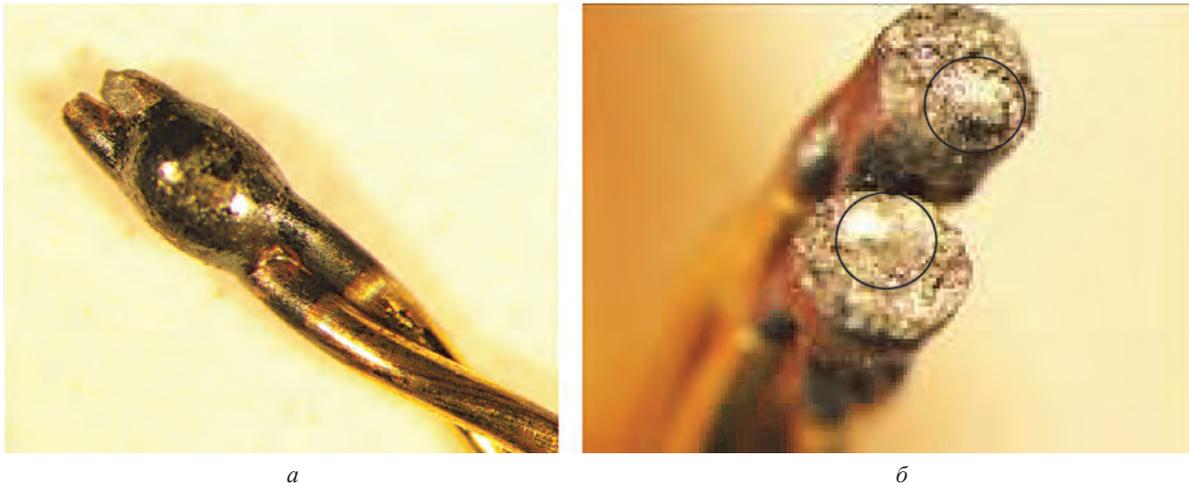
Внешний вид разрушения сварки после испытания на растяжение: *а* – пластичное разрушение в зоне термического влияния; *б* – хрупкое разрушение в зоне сварного шва из-за наличия внутренней полости
